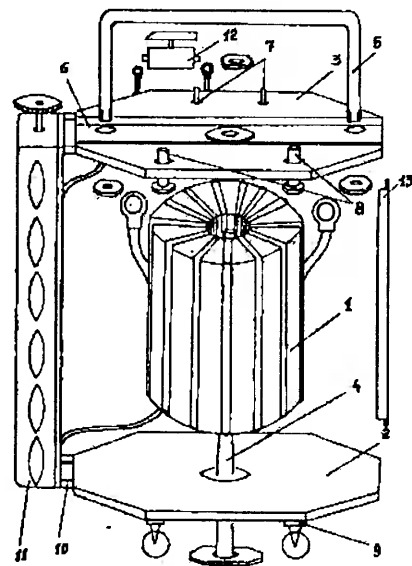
Малогабаритный сварочный трансформатор с тороидальным сердечником:
